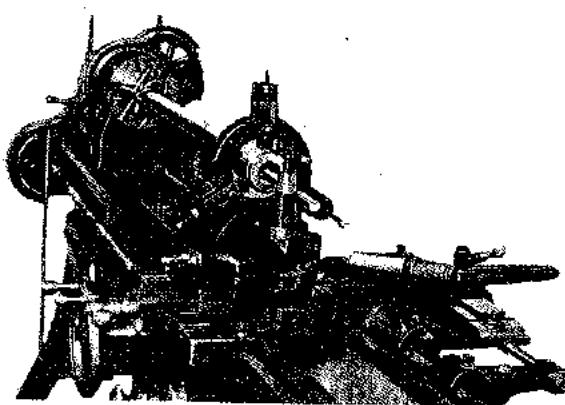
Mandrinado cónico de un agujero con el aparato de tornear cónico (South Bend Lathe Works).
